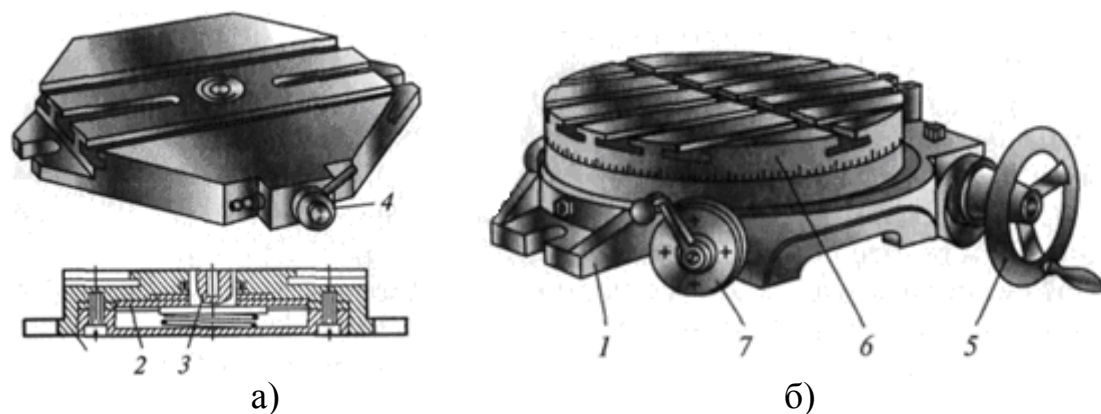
Неповоротний (а) та поворотний (б) столи фрезерного верстата: 1 – основа стола; 2 – мембрана; 3 – шток; 4 – поворотний кран; 5 – штурвал; 6 – стіл; 7 – пневмокран
